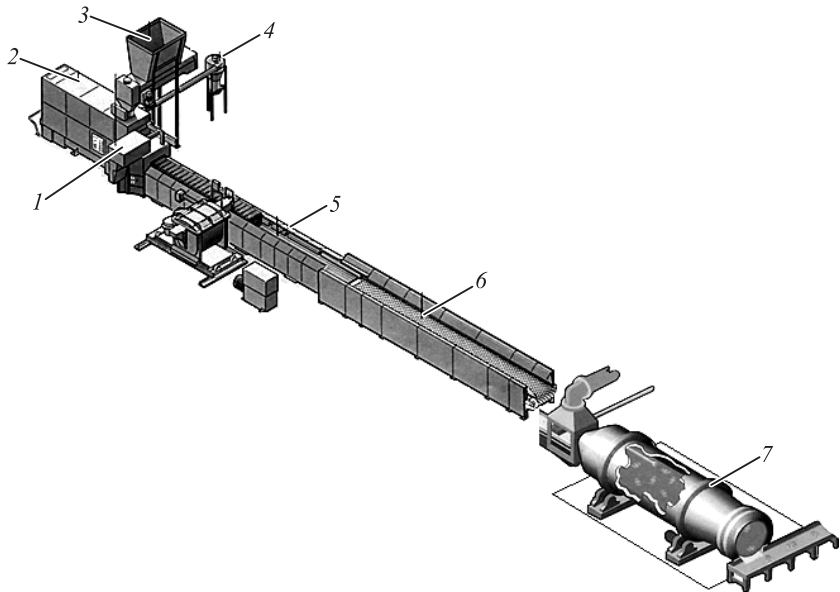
Устройство автоматической формовочной линии вертикальной формовки «DISAMATIC»:
